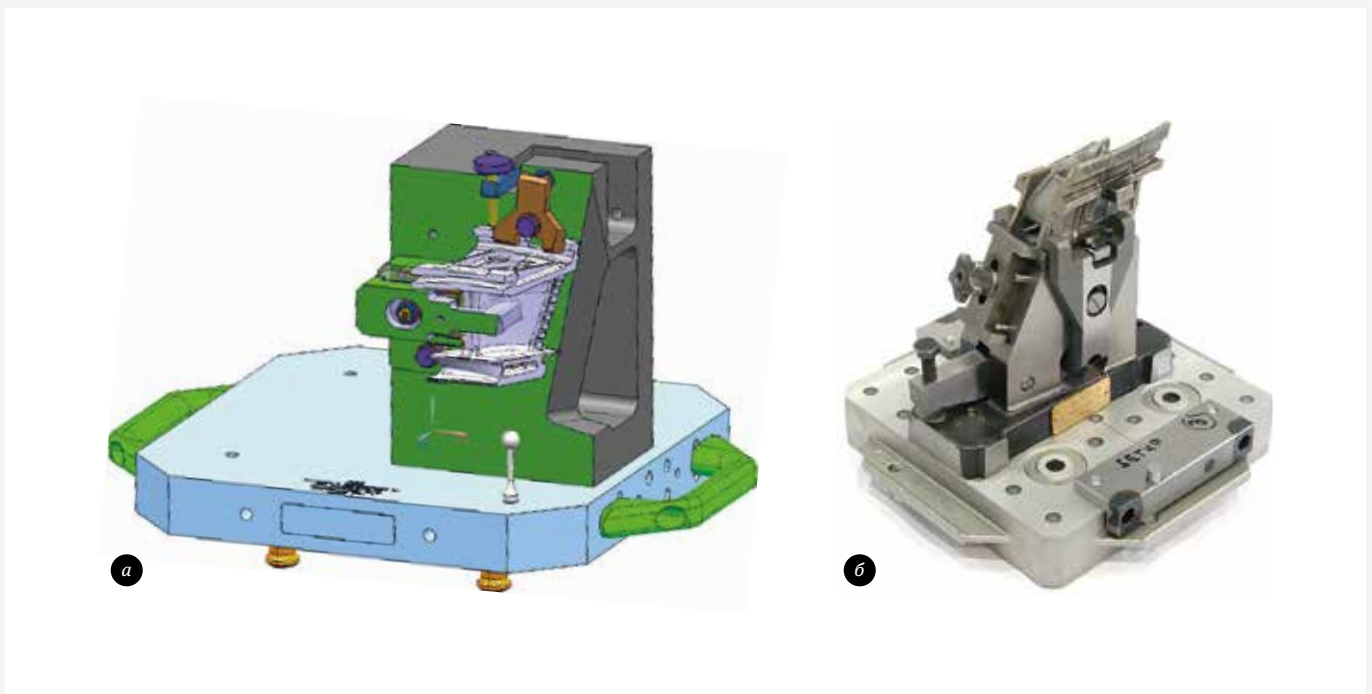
Станочное поворотное приспособление для установки, разворота и обработки базовых установочных поверхностей сопловых лопаток методом глубинного шлифования на станке Magerle MFP-050.65.653-D: *а* – модель; *б* – общий вид
